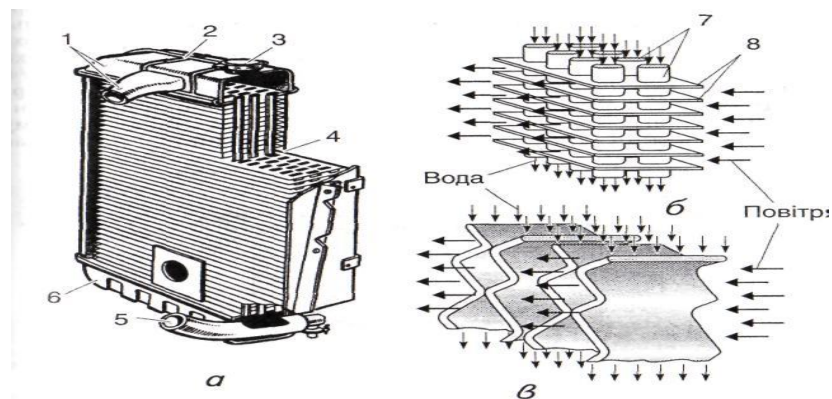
Радіатор: а - будова; б - трубочаста сердцевина; в - пластинчаста сердцевина; 1 - верхній бачок з патрубком; 2 - паровідвідна трубка; 3 - заливна горловина з пробкою; 4 - сердцевина; 5 - патрубок із зливальним краником; 6 - нижній бачок; 7 - трубки; 8 - поперечні пластини
